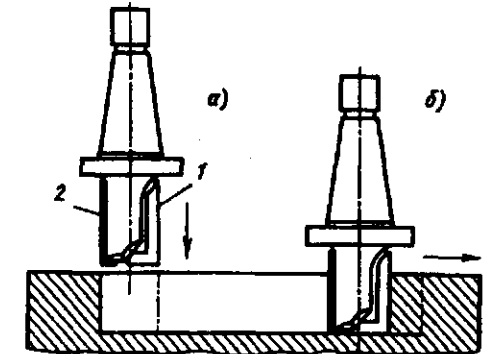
Обработка закрытого шпоночного паза сверлопазовой фрезой фирмы Вальтер (ФРГ)
